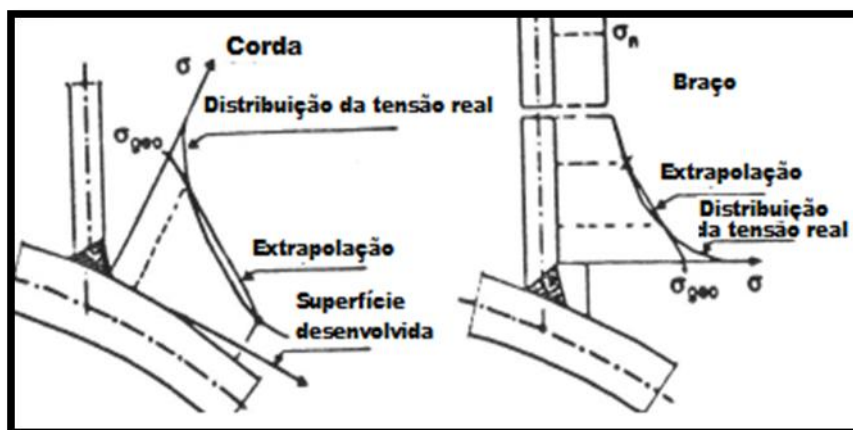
Localização dos extensómetros em estruturas tubulares (adaptado de [16])
